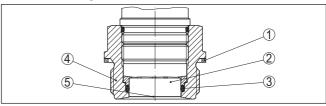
Frontbündiger Einbau der Messzelle (Beispiel: Gewinde G1½)
